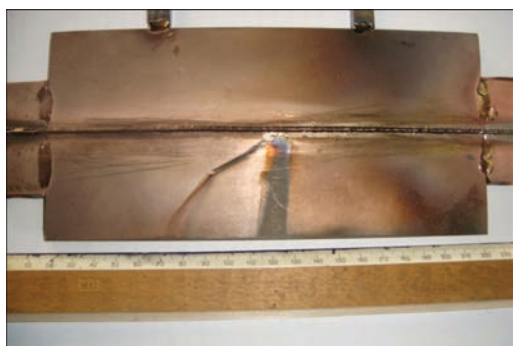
Сварное соединение псевдо-β-титанового сплава BT19, выполненное ЭЛС со стороны корня шва
